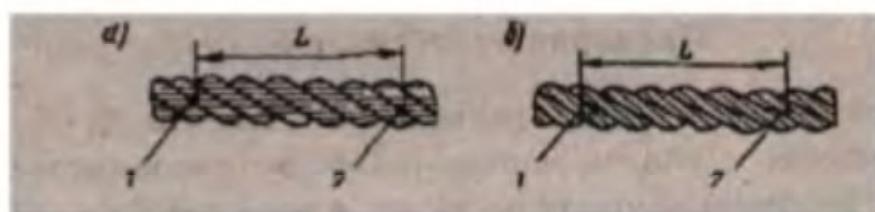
Шаг свивки каната: а - канат крестовой свивки; б - канат односторонней свивки; L - шаг свивки
